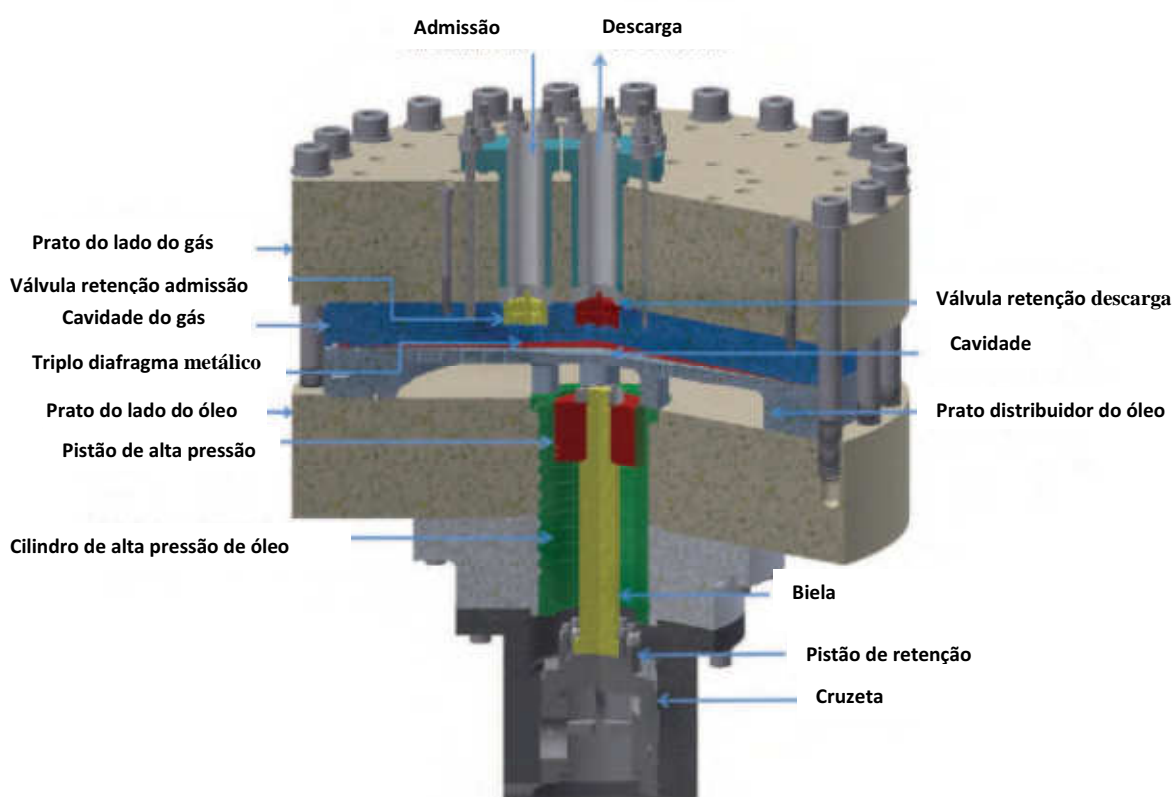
Vista em corte de compressor de diafragma (Fonte: PDC Machines)
